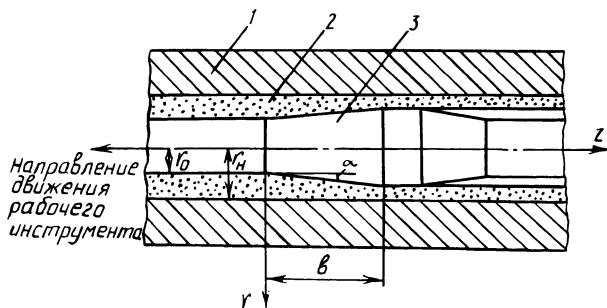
Схема калибрования пористой трубчатой заготовки по внутреннему диаметру:
